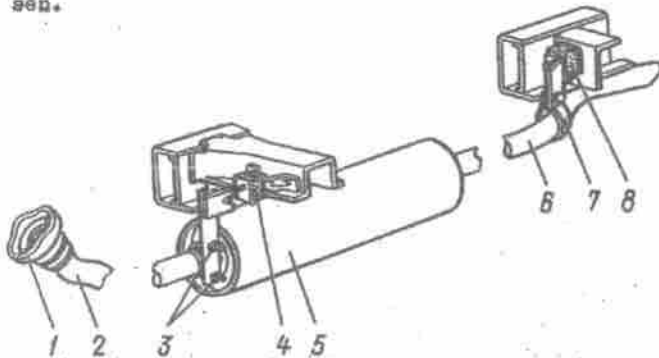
Bauteile des Abgassystems des Kraftwagens VA3-451M und seiner Modifikationen: 1 - Flansch; 2 - Auspuffrohr; 3 - Teile für Befestigung des Auspuffrohrs am Schalldämpfer; 4, 8 - Aufhängungsklassen; 5 - Schalldämpfer; 6 - Auspuffrohr; 7 - Trägern
